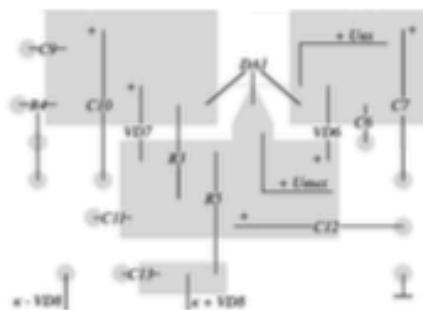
Эскиз монтажной платы стабилизатора 5 В. Вид со стороны расположения деталей
